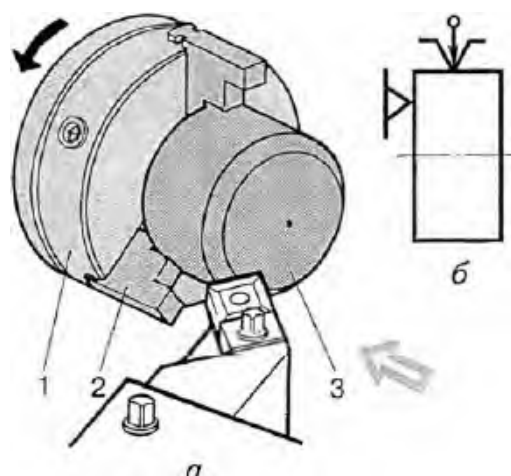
Закріплення заготовки в перевернутих кулачках патрона
